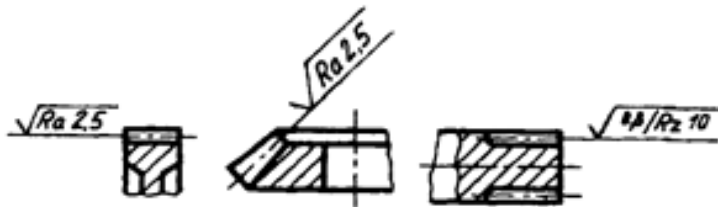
Простановка шероховатости для зубьев зубчатых колес и эвольвентных шлицов
